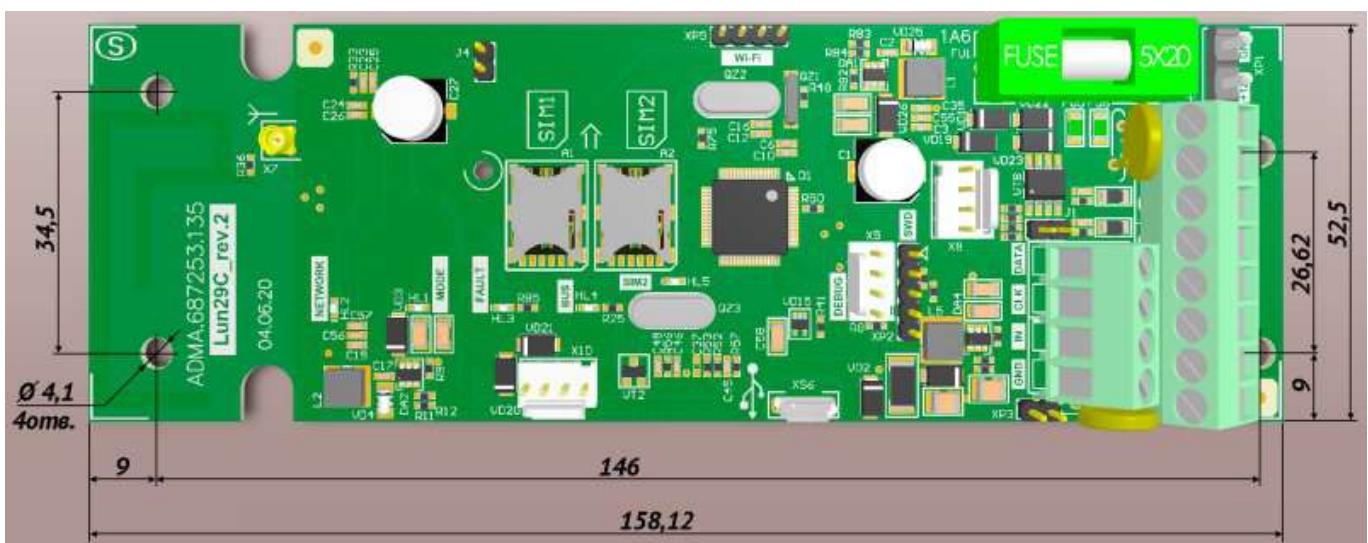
Габаритные и присоединительные размеры платы УСО
